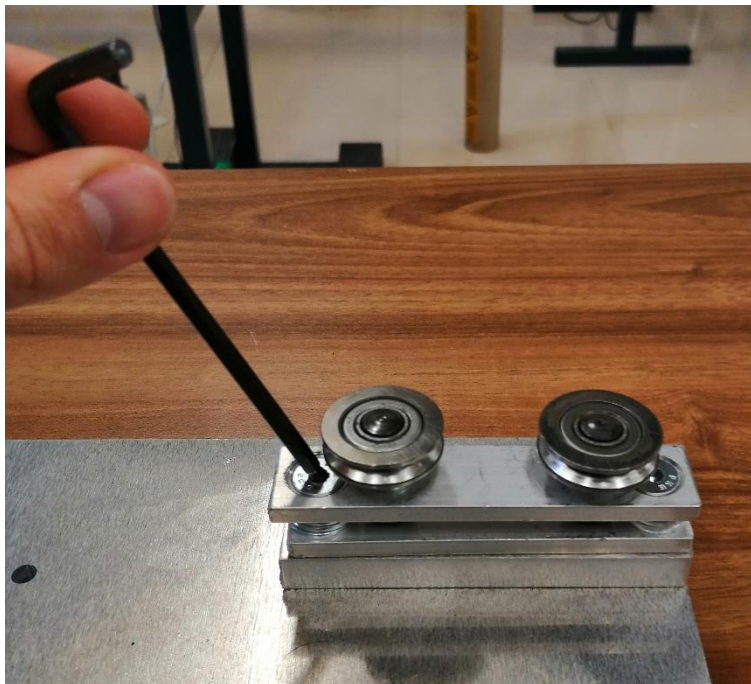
Detalle de la fijación de los zancos a la placa inferior mediante una llave Allen de cabeza redonda
